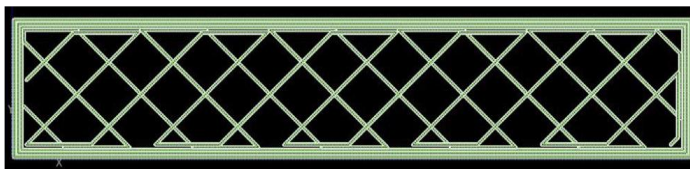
Разреженный-двойной плотный тип детали внутреннего стиля
